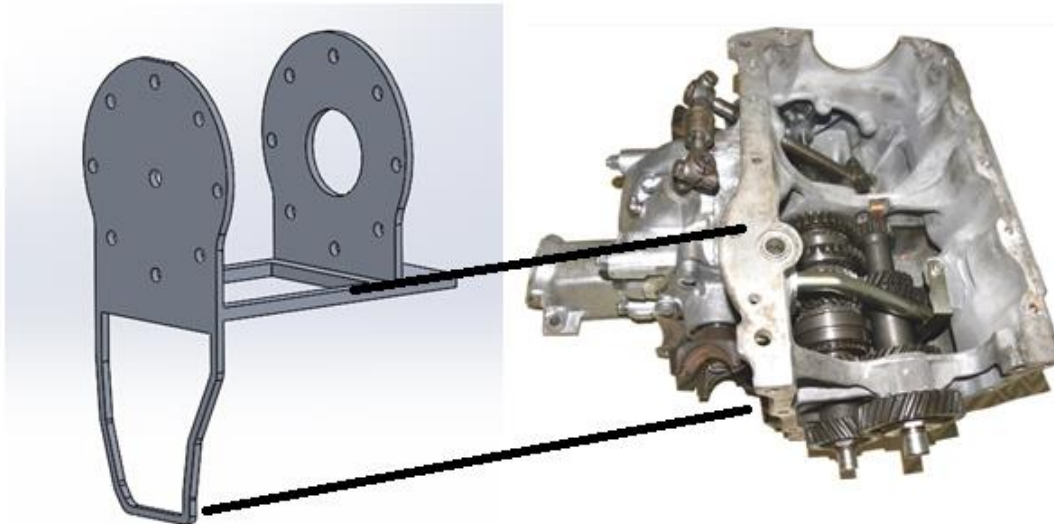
Adaptador motor eléctrico-caja de cambios SolidWorks. Izq.: diseñado por la autora para este TFG. Der.: caja cambios Mini 1275 GT
